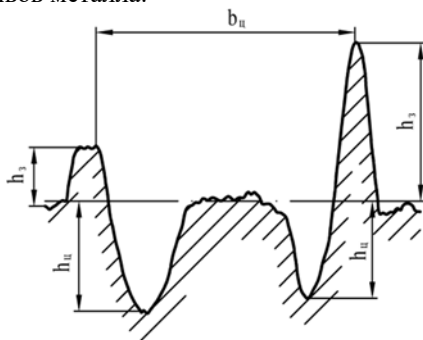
Формы поперечного сечения микроцарапины, полученной при микроцарапании поверхности образца напылами металла с различной высотой режущих кромок
